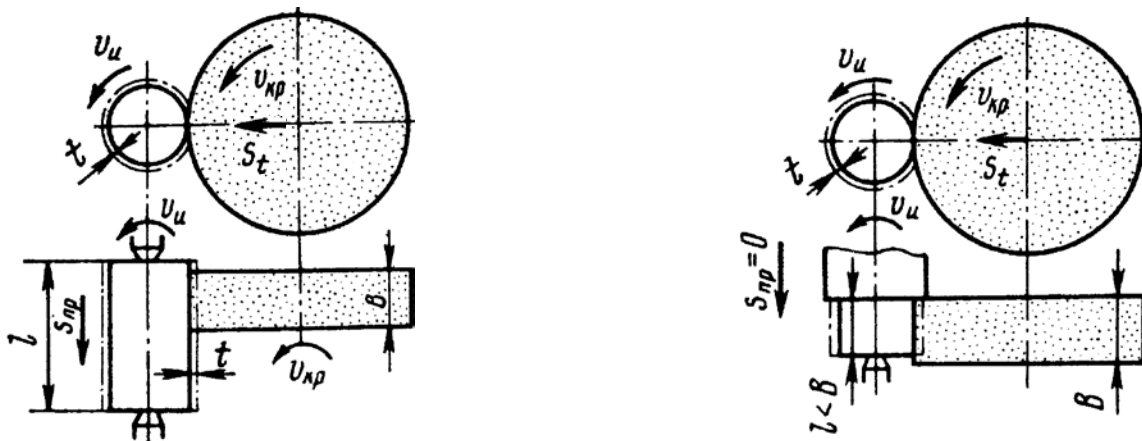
Шліфування циліндричної зовнішньої поверхні:
